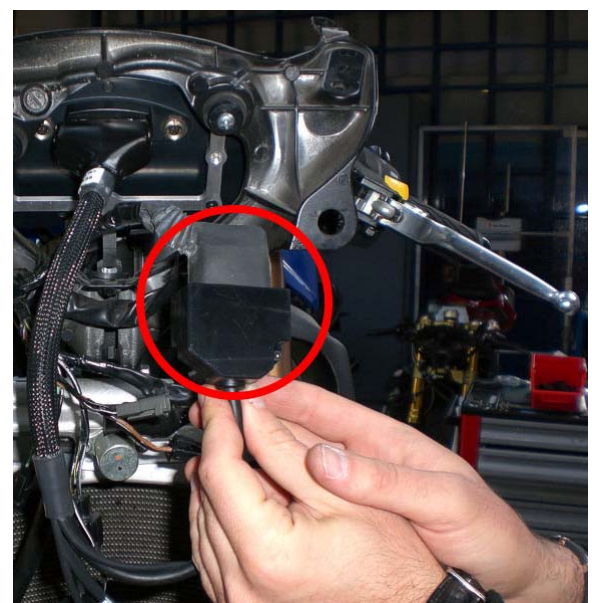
installazione della cuffia in gomma di impermeabilizzazione cablaggio.
